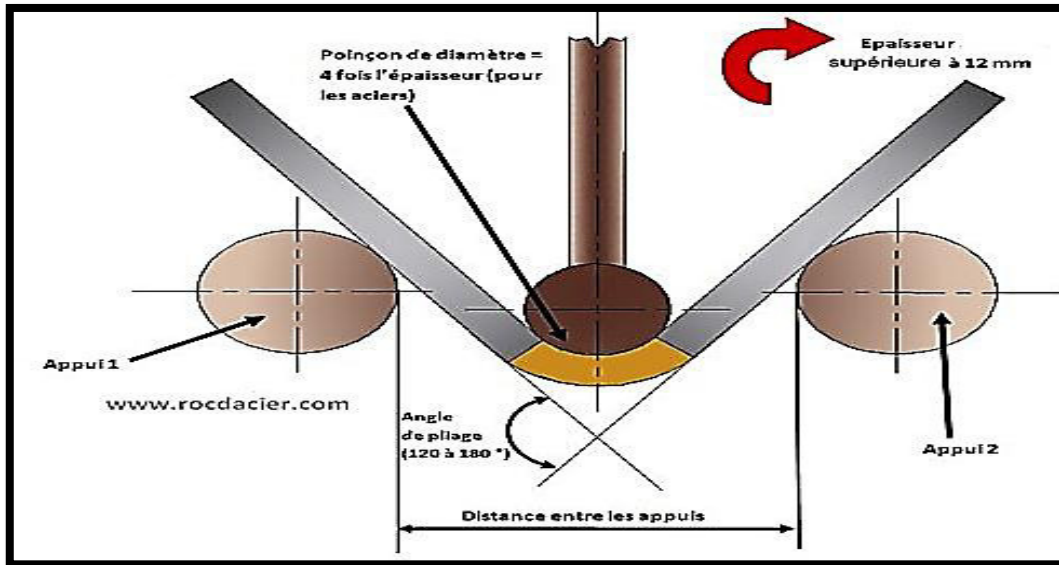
Essai de pliage sur joint soudure.
